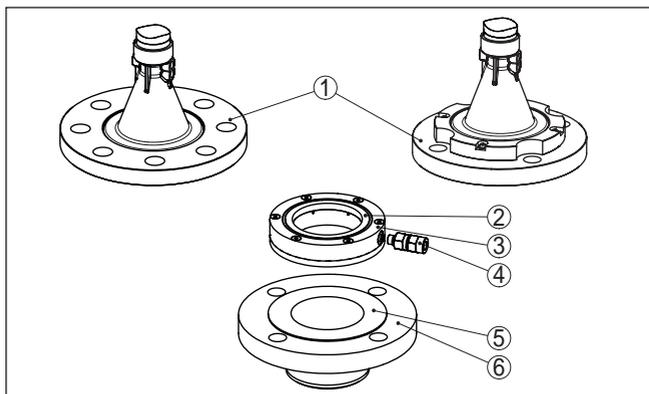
Montagem da conexão de limpeza em flange de capa e flange adaptador ASME 3"
